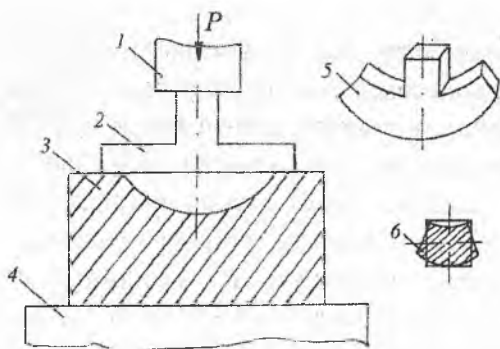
Схема гибки: 1 - верхний боек, 2 - заготовка, 3 - штамп подкладной, 4 - нижний боек, 5 - готовая поковка, 6 - искажение сечения
